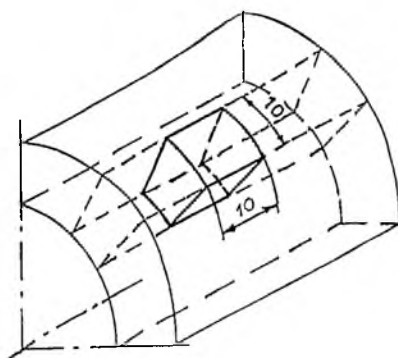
Схема вырезки образцов (размеры приведены в мм).
